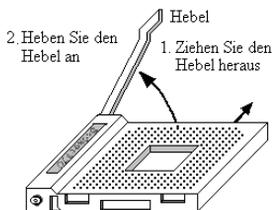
Socket 370 mit geöffnetem Hebel.
